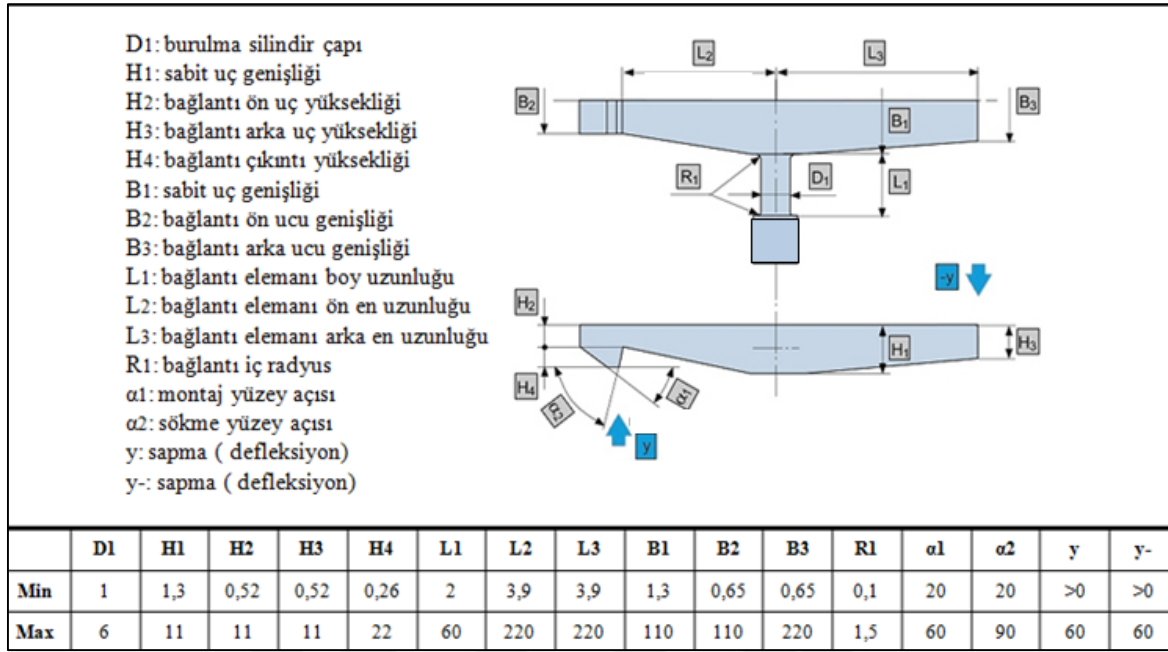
L tipi esneyerek kilitlenen bağlantı elemanının boyutlandırılması [42]
